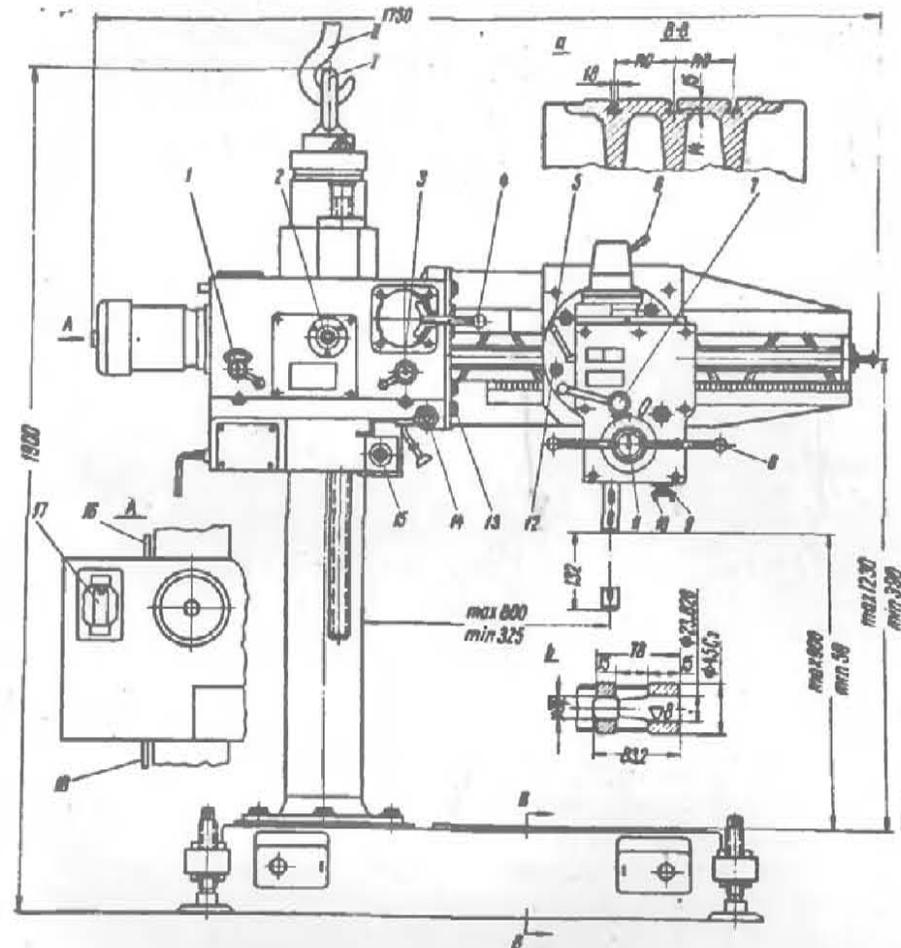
Габаритные размеры станка, рабочего пространства и расположение органов управления:
